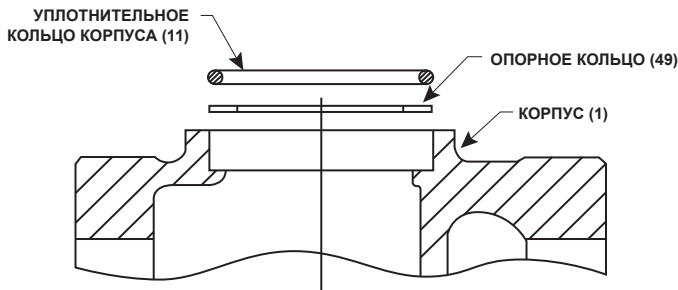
Подetailный вид корпуса с показанным размещением уплотнительного кольца корпуса и опорного кольца
